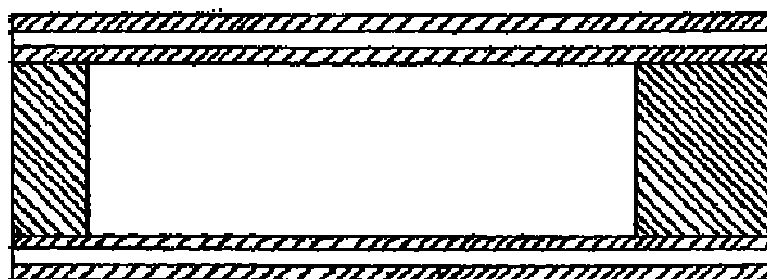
Dois laminados, colados sobre um gradeado. Construção própria para arma.
